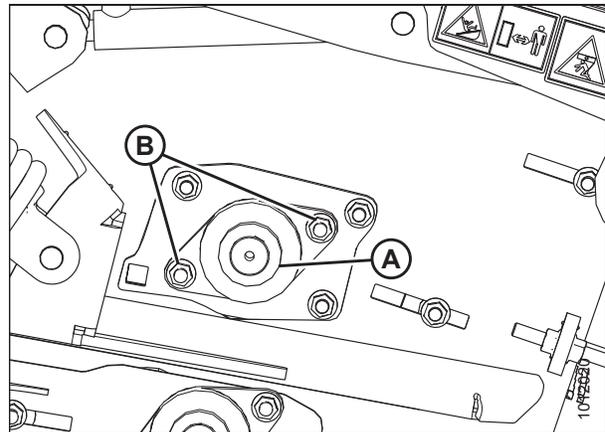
Rodillo de mando de la plataforma frontal derecha
